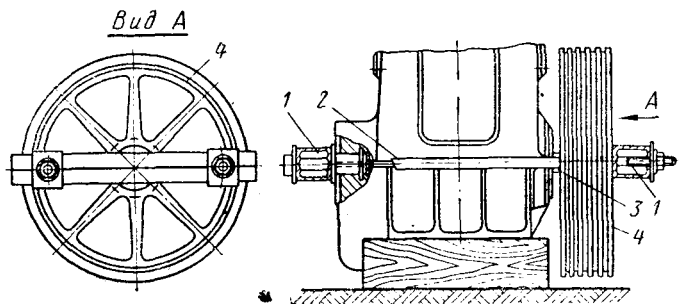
Приспособление для насадки шкивов на валы компрессора и электродвигателя:
